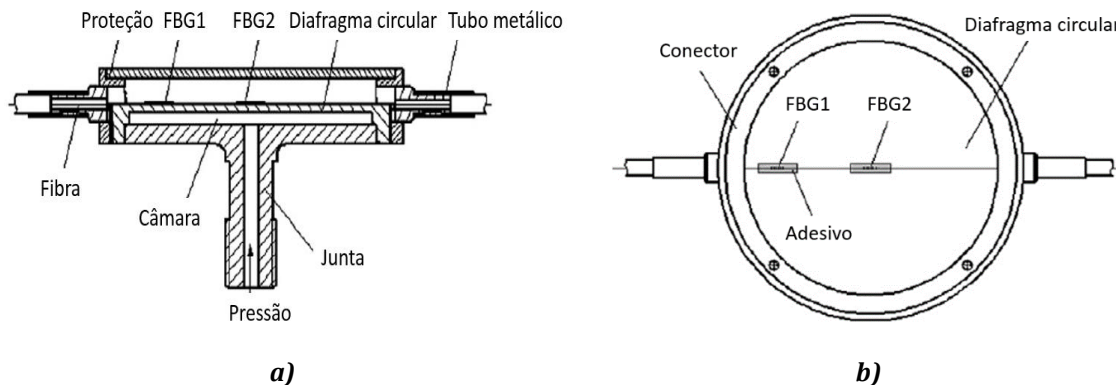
Esquema do sensor apresentado por Huang *et al.*: a) Vista em corte. b) Vista de topo. Adaptado de [23].
